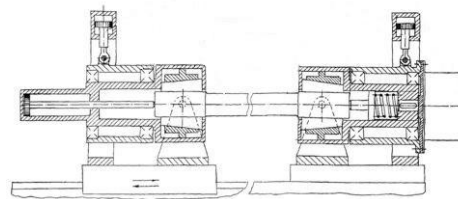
Конструктивная схема установки для динамической стабилизации труб
